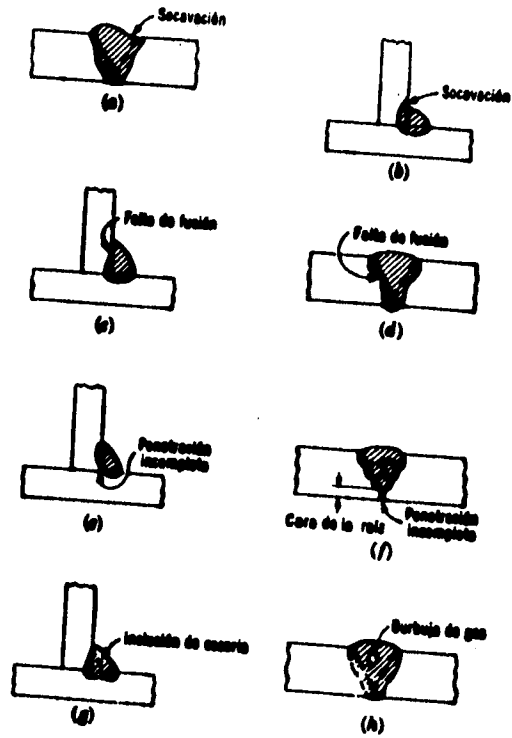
DEFECTOS DE SOLDADURA
